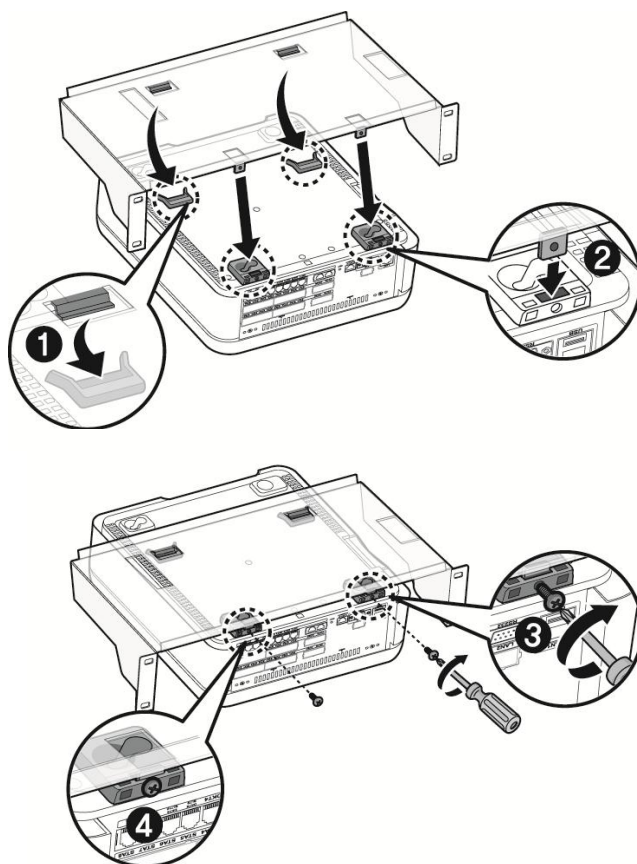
Установка монтажного шаблона и настенный монтаж
